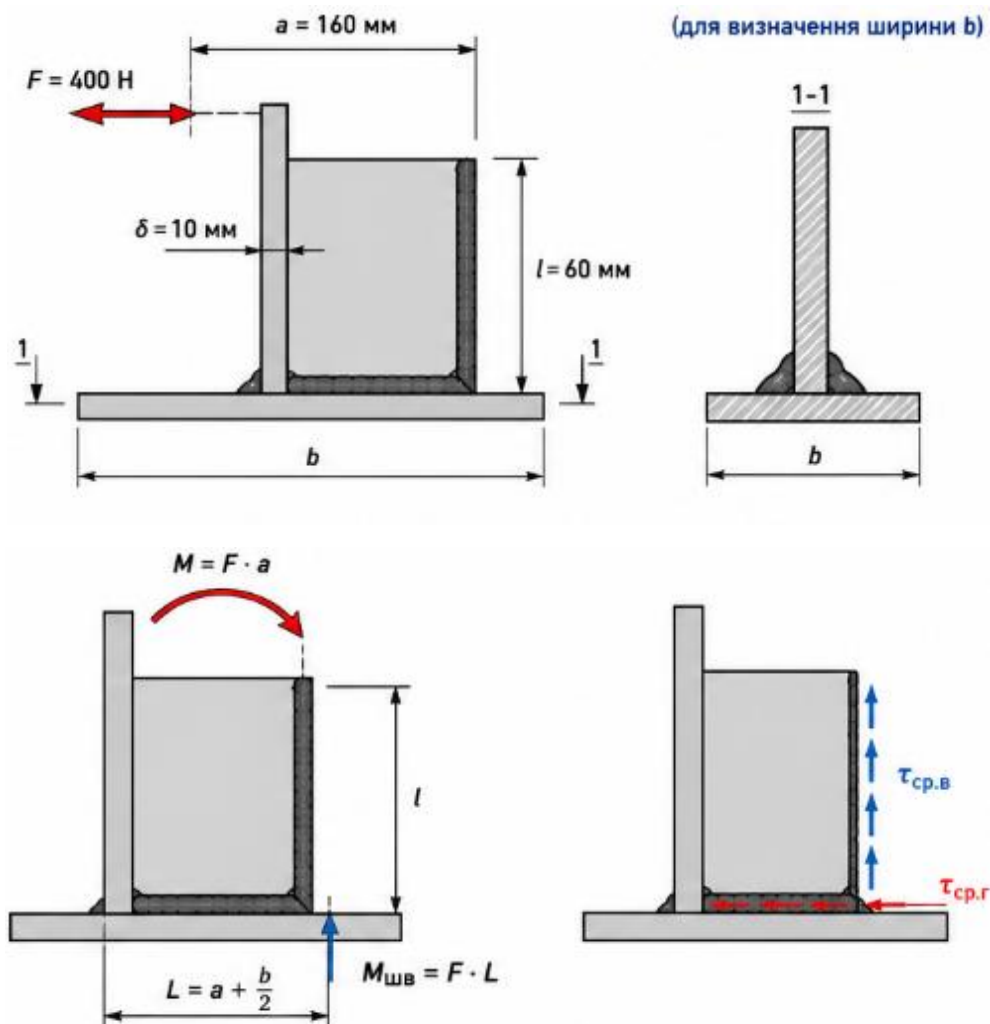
Схема до розрахунку міцності зварного з'єднання
